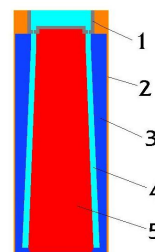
Отливка «Втулка коническая»: 1 – чаша из ПСС; 2 – воздух; 3 – кокиль; 4 – отливка; 5 – стержень из ПСС
